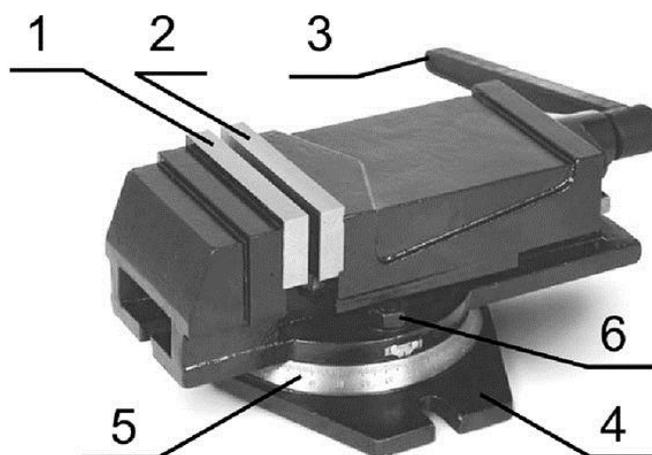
Поворотные тиски: 1 - накладка неподвижной губки; 2 - накладка подвижной губки; 3 – ручка; 4 - основание с пазами для крепления тисков; 5 – лимб; 6 - гайка зажима поворотного механизма тисков.
